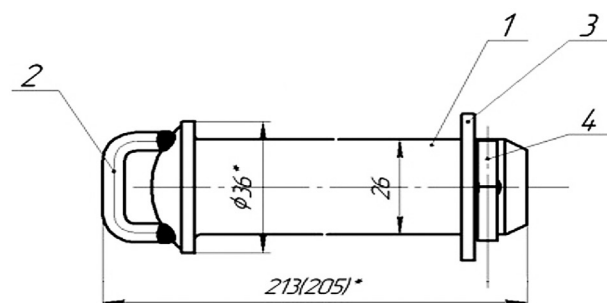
Ось соединительная с приваренной ручкой: 1 — ось; 2 — ручка; 3 — шайба; 4 — шплицт
